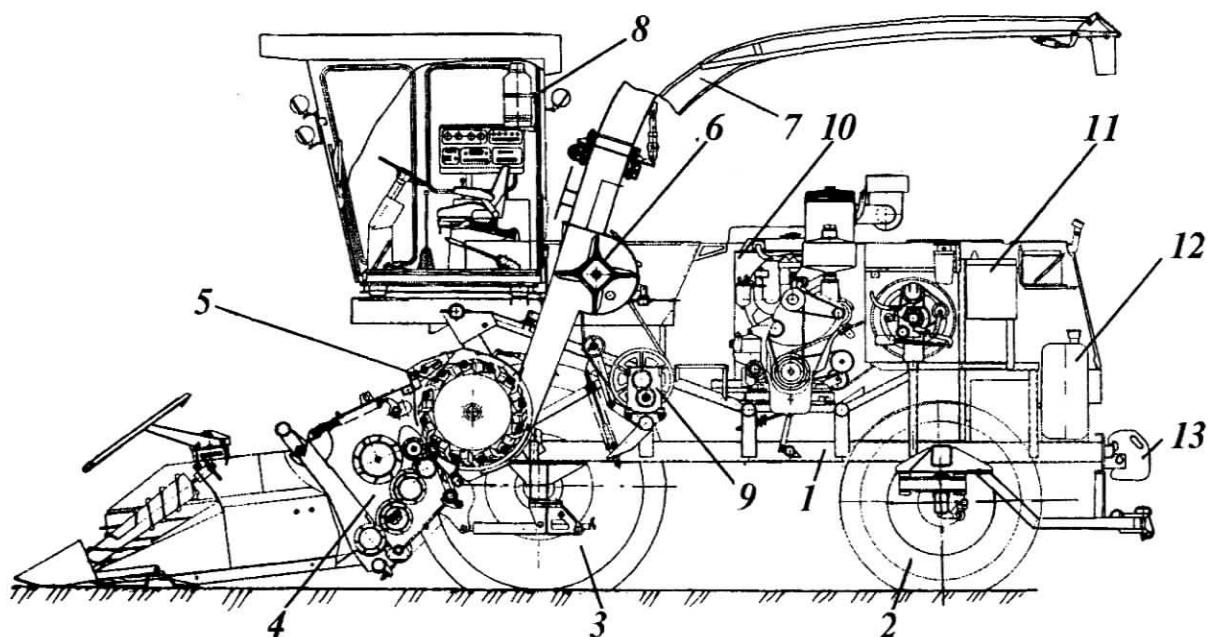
Комбайн кормоуборочный самоходный (продольный разрез)
